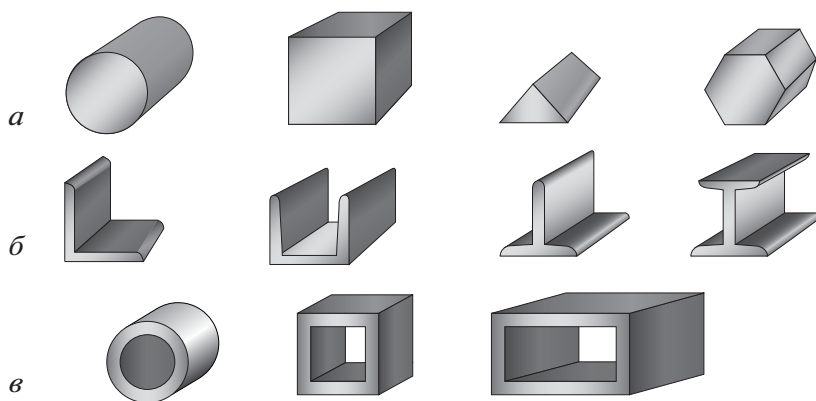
Металлические профили: *а* — сортовые профили правильной геометрической формы; *б* — сортовые фасонные профили; *в* — трубы
